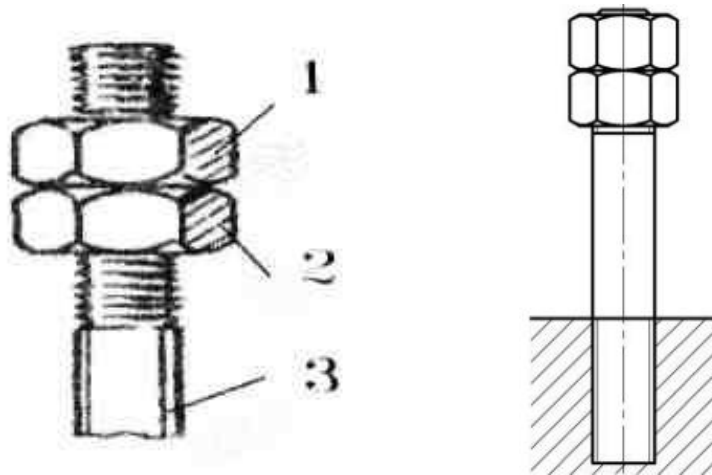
Спосіб викручування шпильки двома гайками: 1- гайка; 2- контргайка; 3- шпилька.
